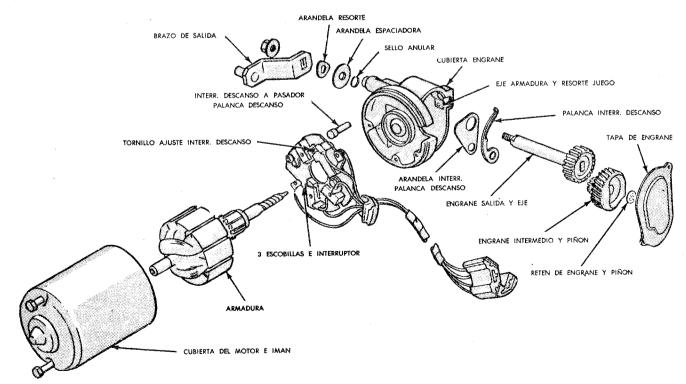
Componentes del Motor de los Limpiadores. Típico.
